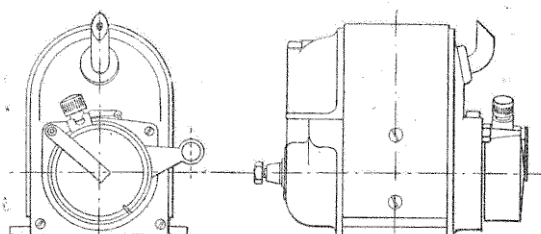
Magnéto Perfecta, vue du côté du rupteur et vue de côté.
